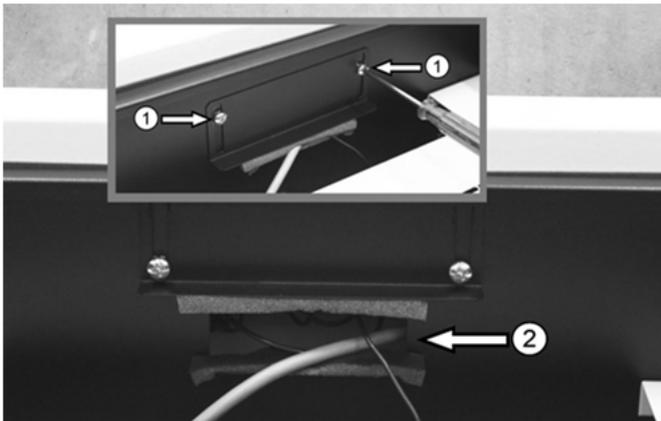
Kabeldurchführung ② am Schaltfeldgehäuse
